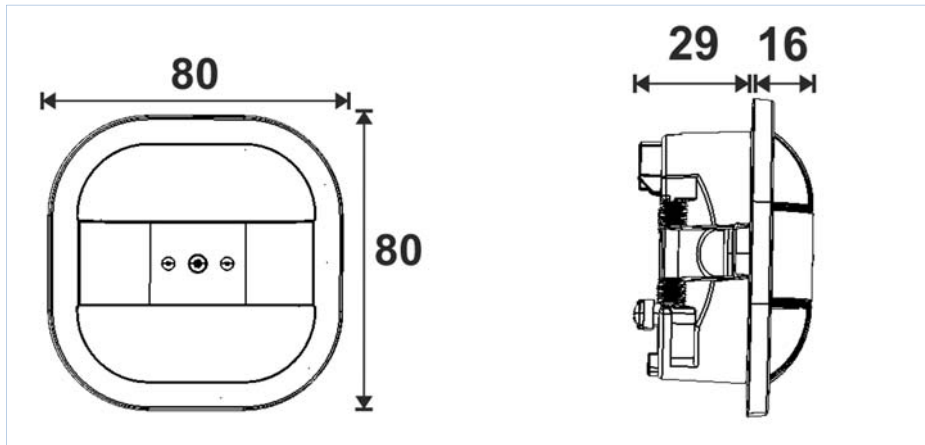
Abmessungen Busch-Präsenzmelder Mini KNX / Busch-Präsenzmelder Mini Premium KNX
